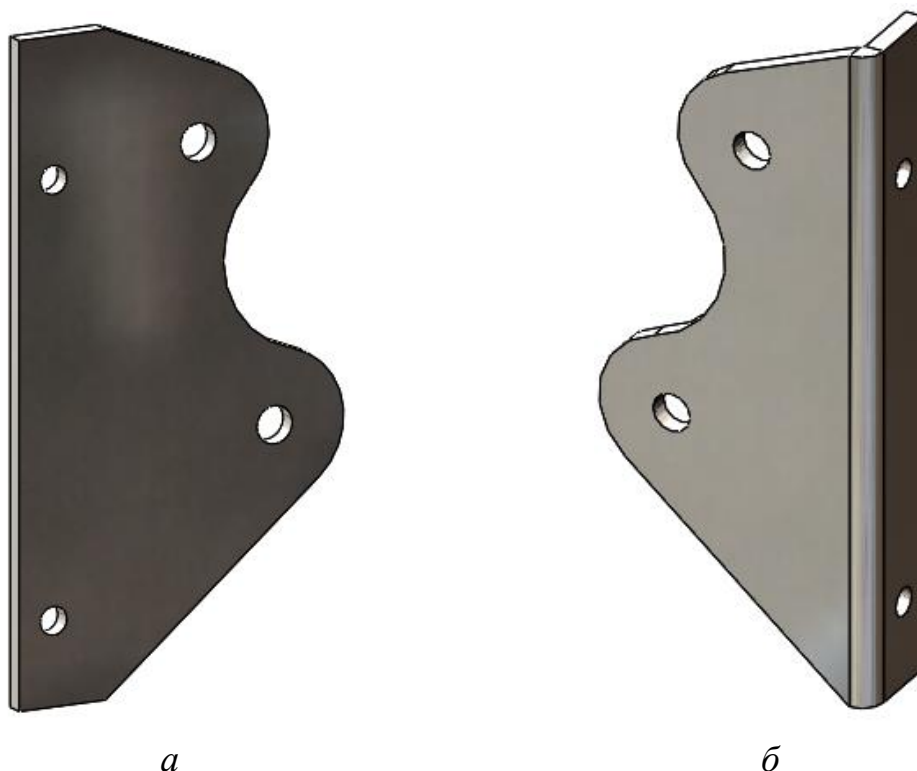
3D модель кронштейна крепления тормозного суппорта. *а* – развертка кронштейна; *б* – форма после листогиба
